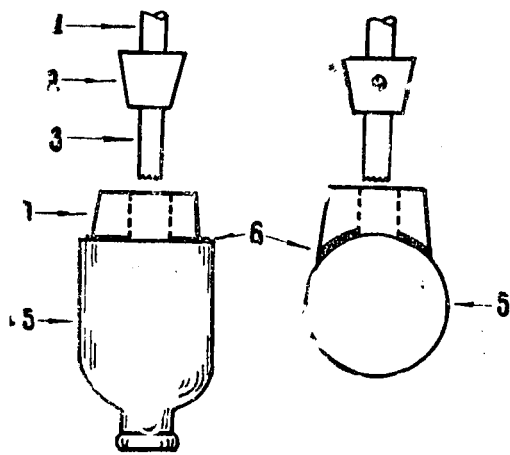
Приклеивание направляющей корковой пробки (4) менделеевской замазкой (6) к стеклянной детали (5); 1 — вал мотора, 2 — соединительная пробка, 3 — трубка-сверло.
